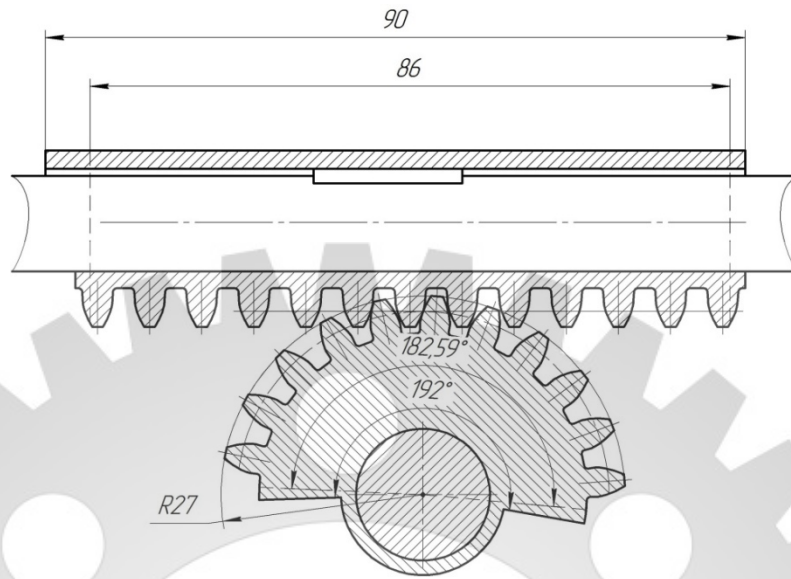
Механізм переключення блоків коробки швидкостей з трьома зубчатыми колесами
